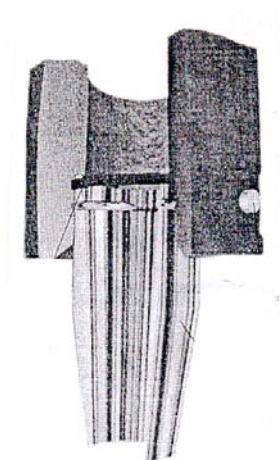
Удлиненные насадки из износостойкого чугуна
